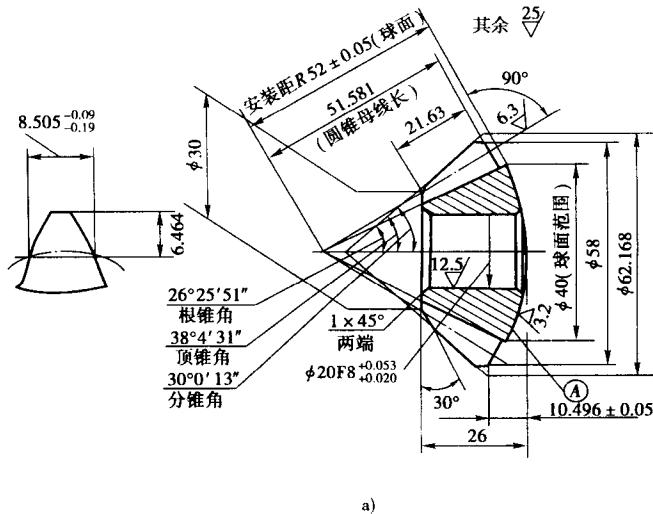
东-20 行星齿轮的零件图和精密锻件图
